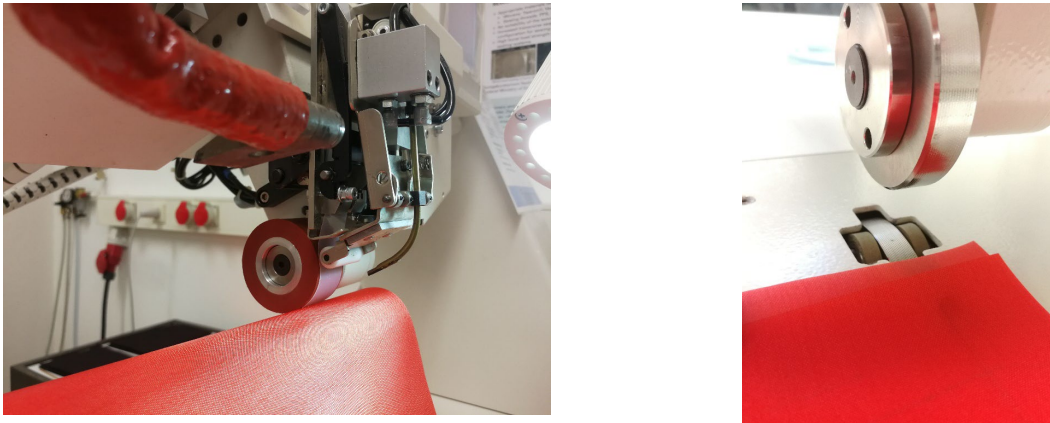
Riverseal © 200 HT auf Heißluft Schweißanlage (links) sowie auf US-Schweißanlage (rechts)
